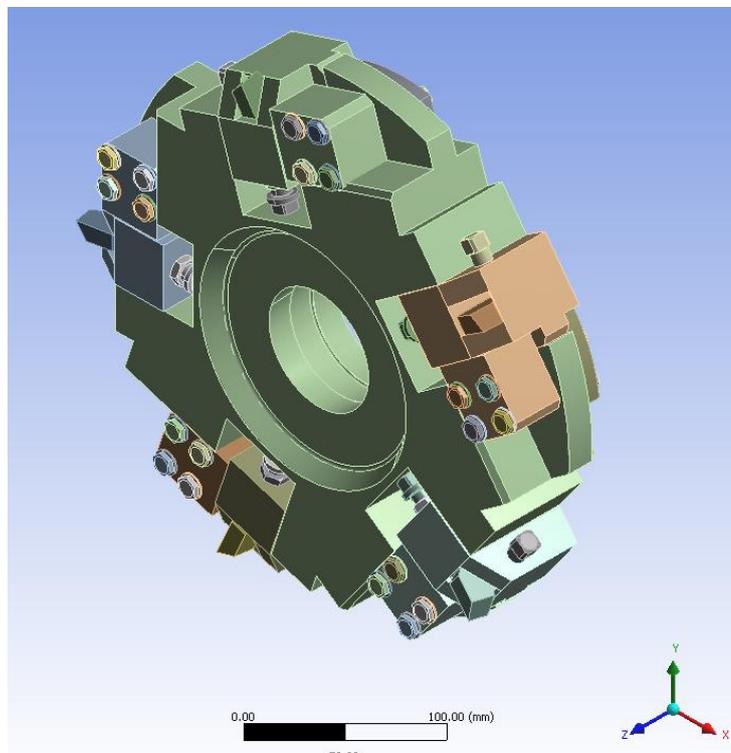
Сборочная модель фрезы (общий вид)
